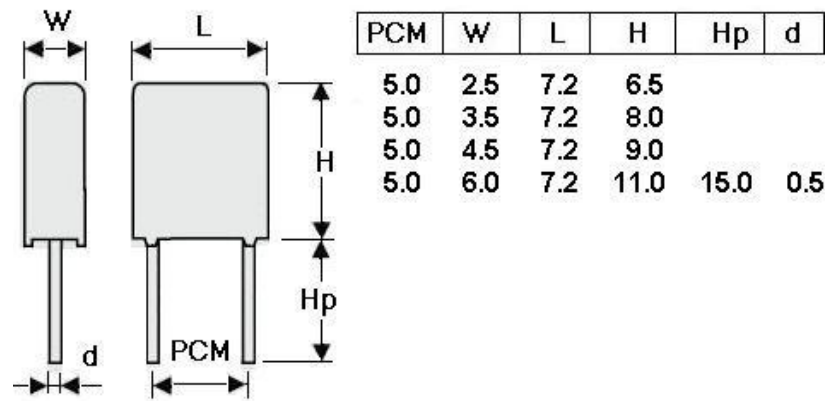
Габаритні розміри конденсатора В32529С1102J000
